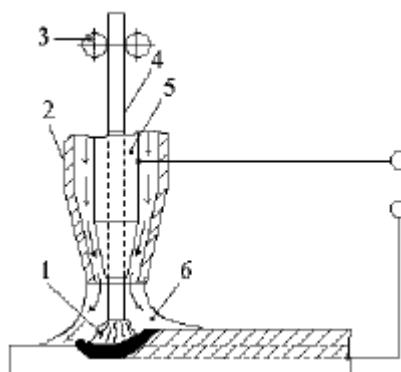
Дуговая сварка и наплавка в защитном газе плавящимся электродом: 1 – электрическая дуга; 2 – газовое сопло; 3 – подающие ролики; 4 – электродная проволока; 5 – токопроводящий мундштук; 6 – защитный газ
